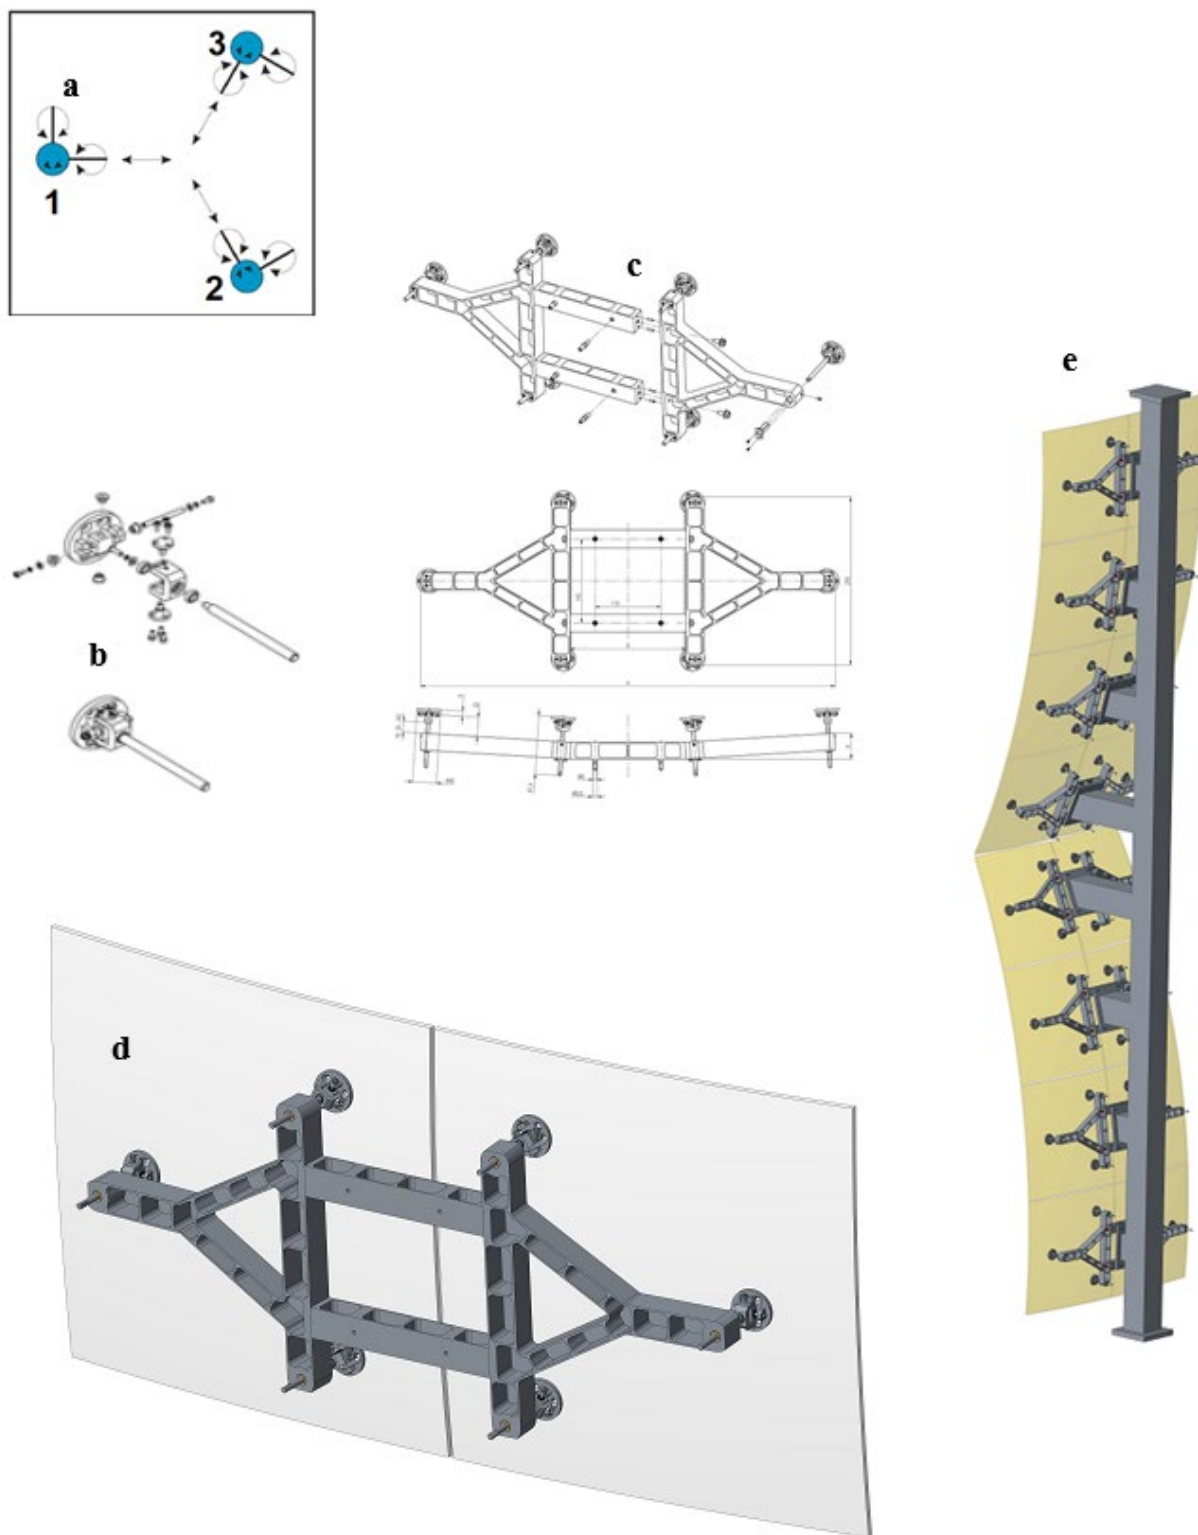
Система поддержки зеркальных плиток: а.- схема 3-х точечного крепления зеркала; б.- механизм поддержки и юстировки зеркал; с.- конструкция рамки крепления 2-х плиток; д.- рамка с установленными двумя зеркальными плитками, е.- колонна, для крепления 2-х рядов плиток
